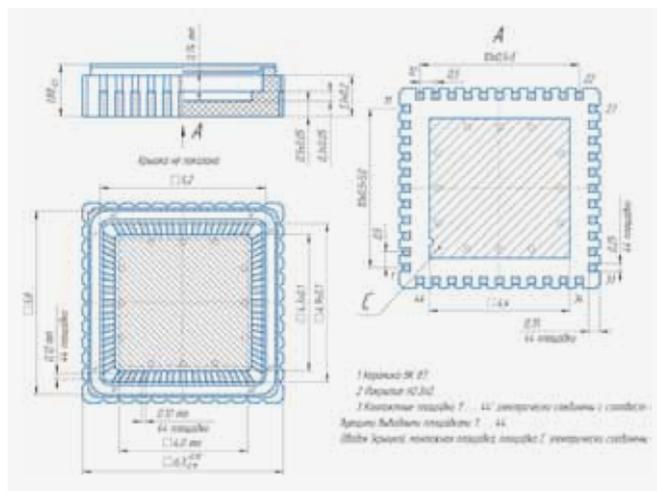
Габаритный чертеж корпуса МК 5165.44-1
